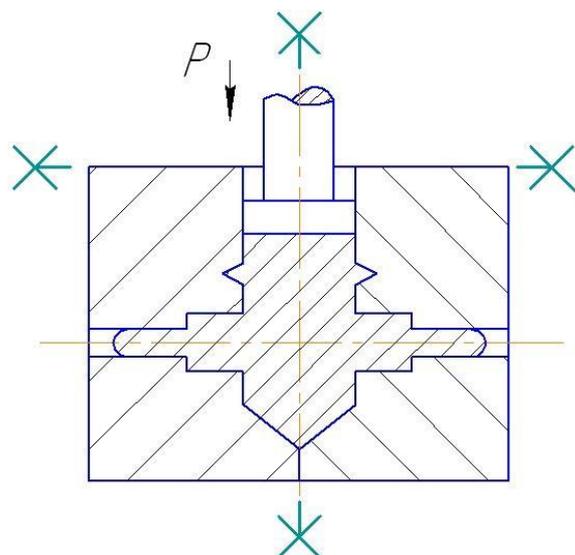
Штамповка поковок прошивкой в разъемной матрице
